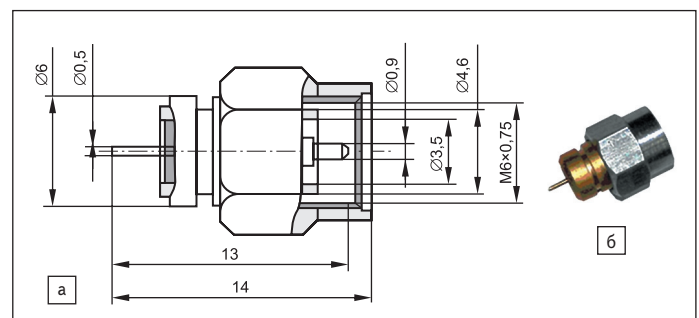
Соединитель TC2.236.074: а) конструкция; б) внешний вид
